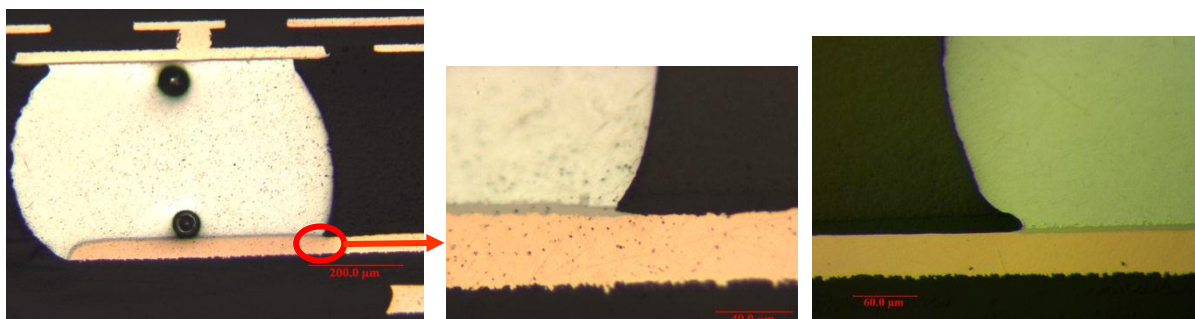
Filière SAC underfill : pas de fissuration au niveau des assemblages
